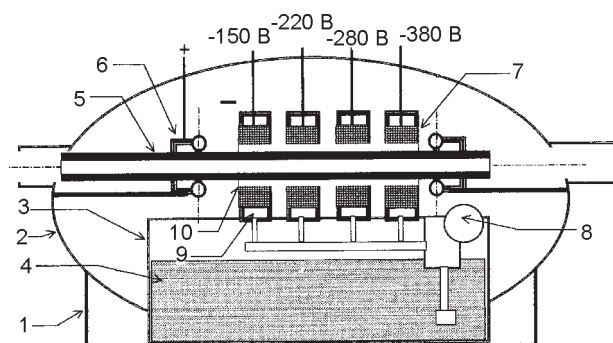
Схема установки для микродугового оксидирования поверхности изделия вытянутой формы.
